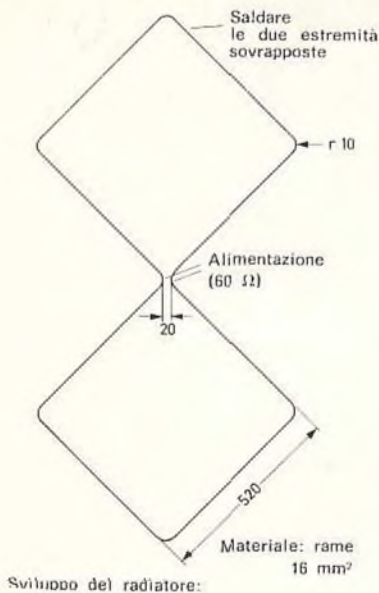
Dimensioni del radiatore di fig. 2a.
